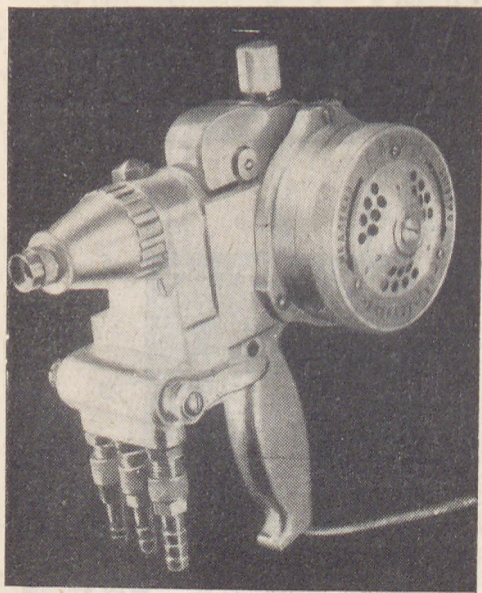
Газовый инжекторный металлатор ГИМ-1
